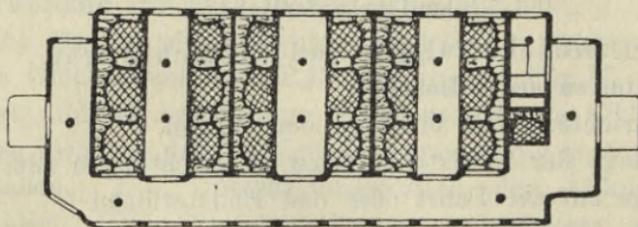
Grundriss eines Eisenbahn-Personenwagens.
